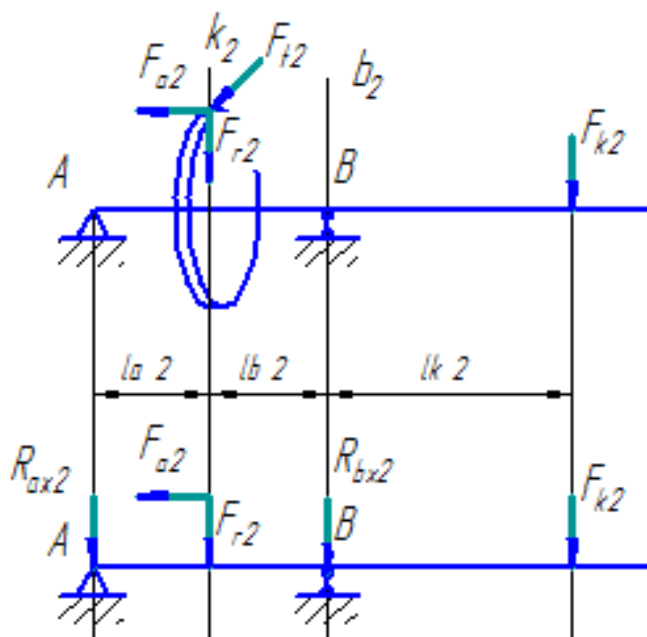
Розрахункова схема черв'ячного колеса
